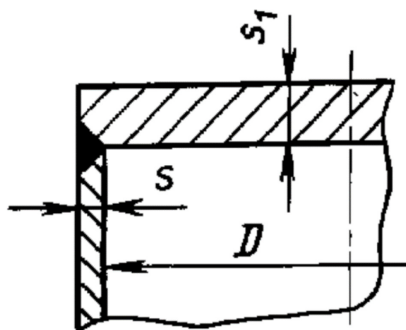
Предполагаемый способ крепления крышки/днища к обечайке [4].
